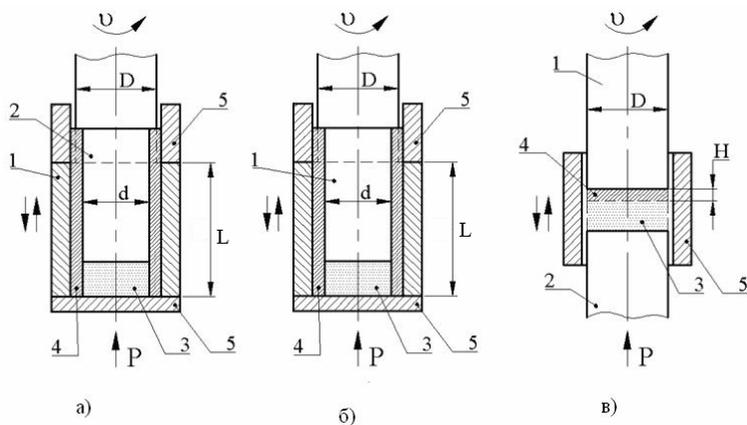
Принципиальные схемы процесса наплавки трением:
